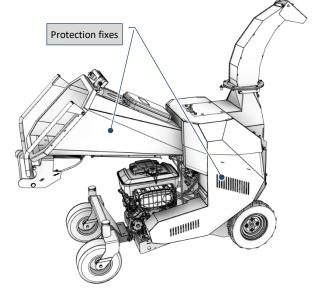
Protections fixes de la machine (vue côté droit)
